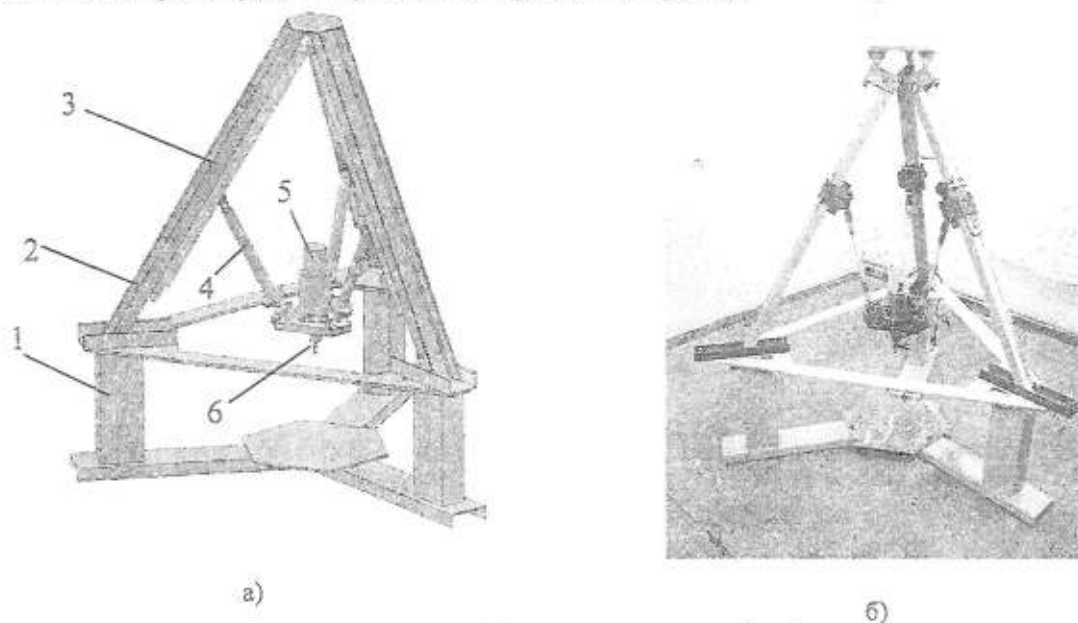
Трикоординатний свердлильно-фрезерний верстат пірамідальної компоновки з МПС і штангами постійної довжини (патент України № 86533): а) – САД модель; б) – виготовлений дослідний макет в ХНТУ: 1 – основа; 2 – каркас; 3 – напрямна з приводом подачі; 4 – штанга; 5 – мотор-шпindel; 6 – затискний патрон з інструментом
